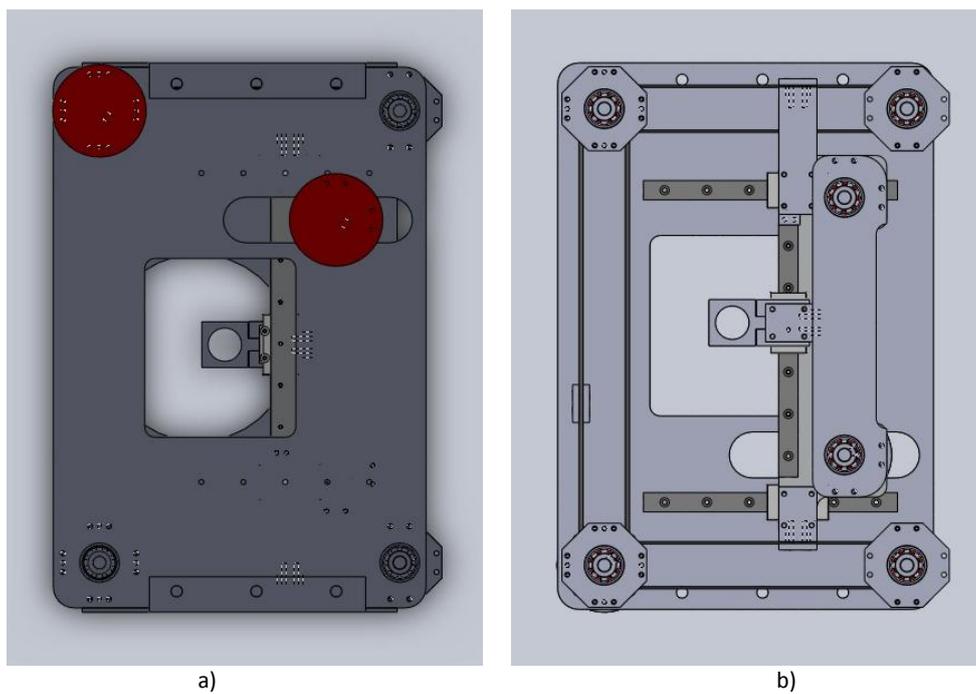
Sistema na posição de ponto morto. a) Vista de cima. b) Vista de baixo.
